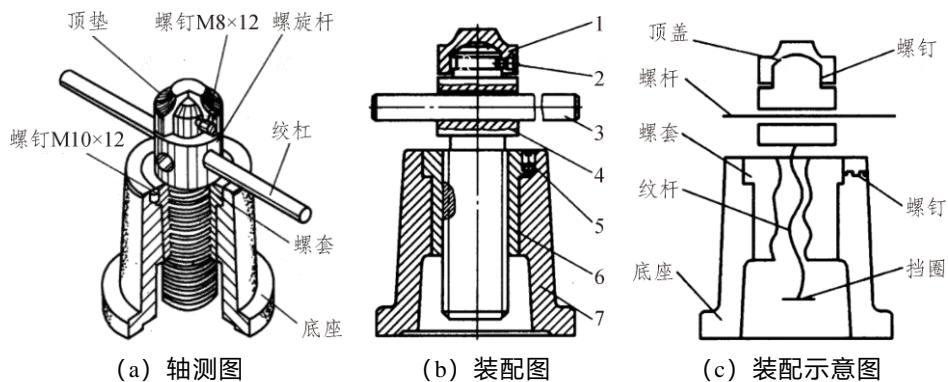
螺旋千斤顶的轴测图、装配图和装配示意图
